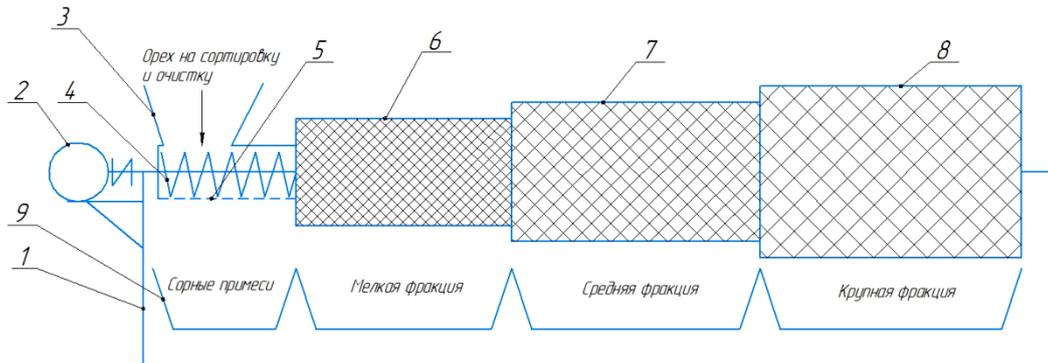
Кинематическая схема нового универсального оборудования для извлечения из шишек кедровых орехов, их очистки и сортировки:
